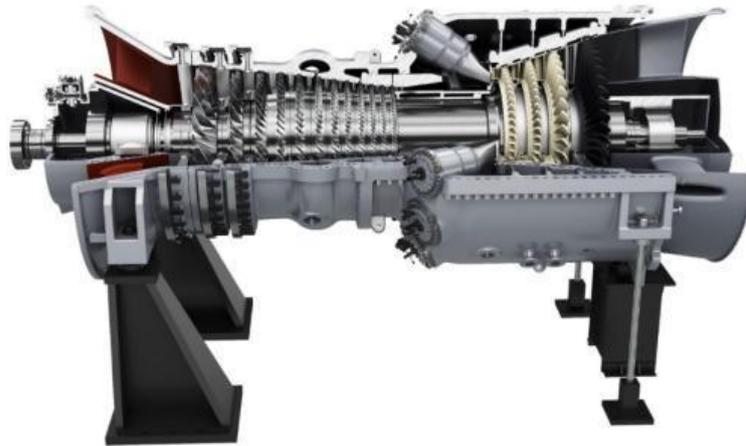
SIEMENS SGT6-9000HL
